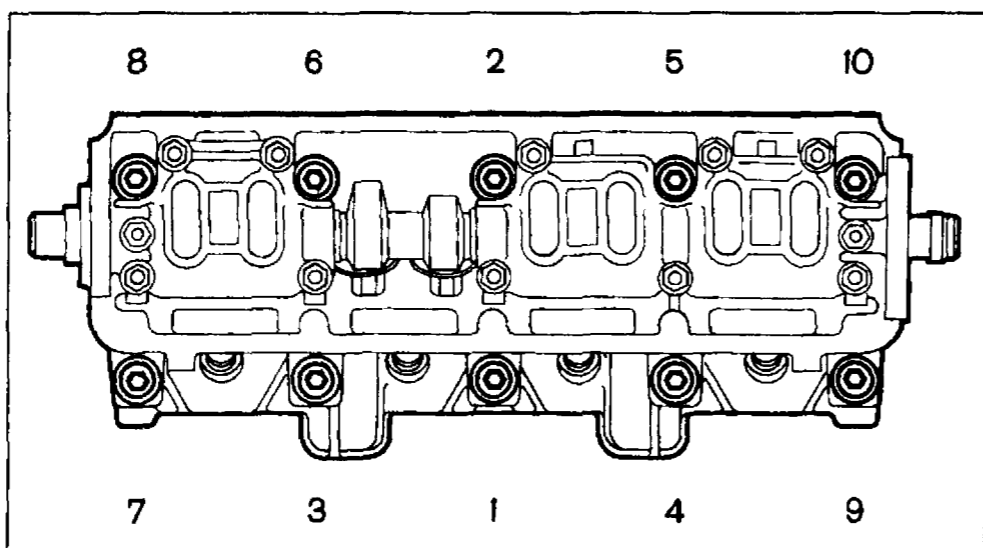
Порядок затягивания болтов головки блока цилиндров
